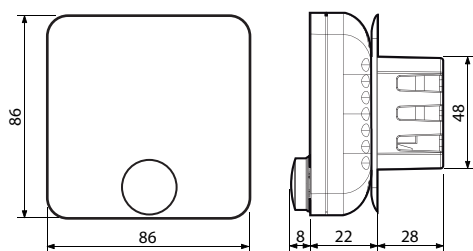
Габаритный чертеж терминала зонального управления для внутристенного монтажа (размеры даны в мм)
